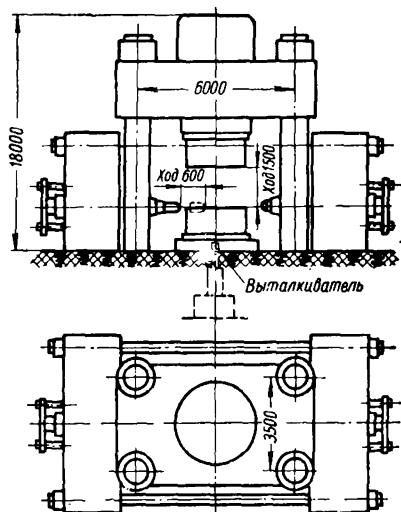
Схема комбинированного гидравлического штамповочного пресса
